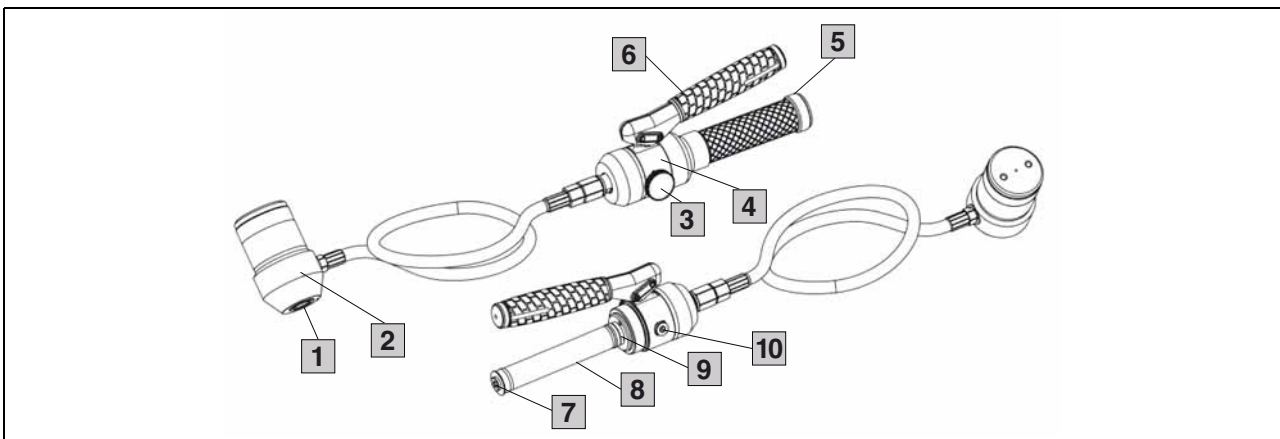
Hand-Hydraulikstanze flexibel, mit Hydraulikschlauch und separatem Zylinder/
